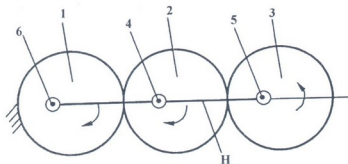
Планетарная передача с эксцентричными круглыми цилиндрическими зубчатыми колесами
